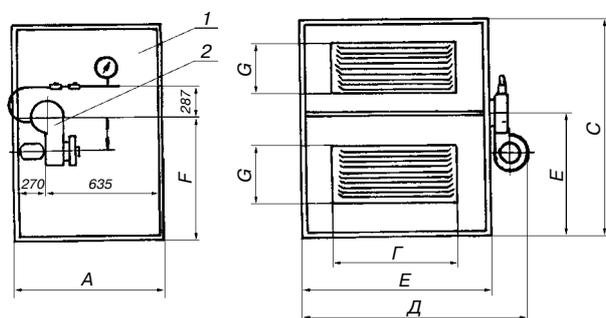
Конструктивные размеры воздухонагревателя ВРК: 1 – корпус воздухонагревателя; 2 – автоматизированная блочная горелка
